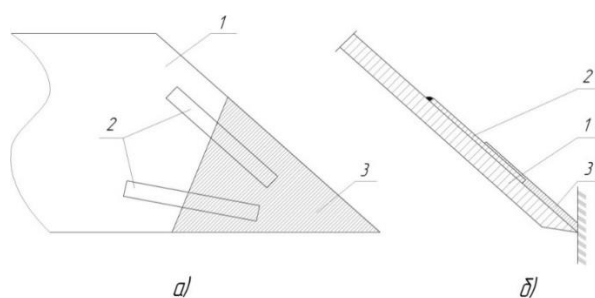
Плужный лемех: а) носовая часть; б) разрез по ребру жесткости, вид сбоку; 1 – основа; 2 – ребра; 3 - наплавка
